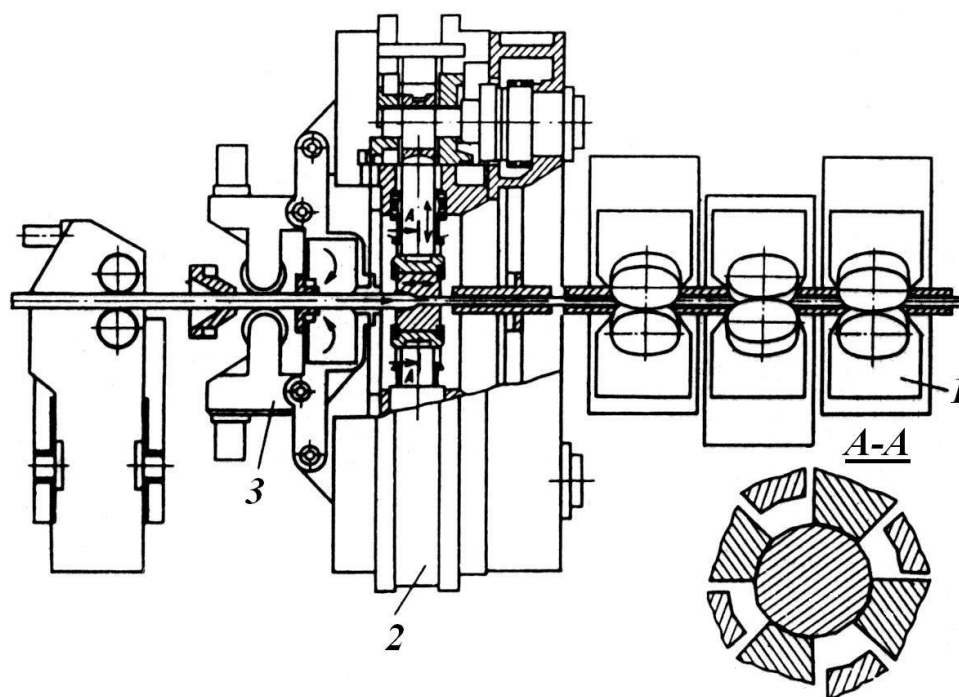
Конструктивная схема ковочно-прокатного агрегата фирмы «GFM»:
